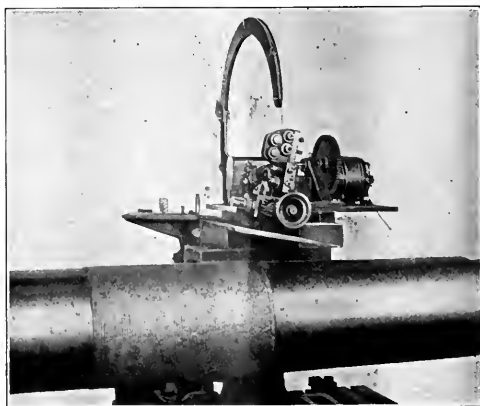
SOLDADORA AUTOMÁTICA
